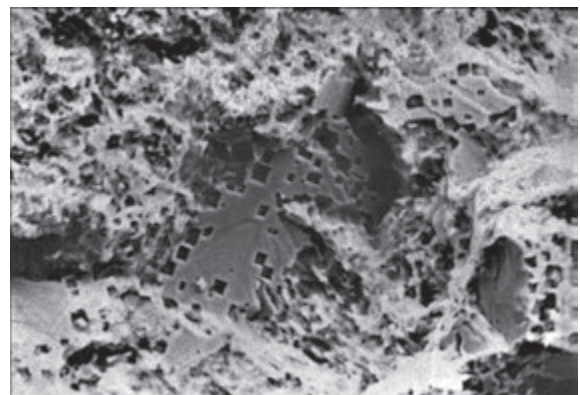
Пори у зварному шві, які виникли за рахунок неякісного зварювання
